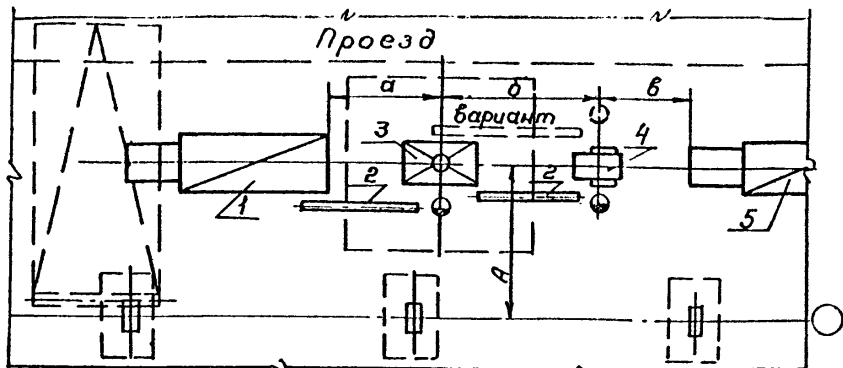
Схема расположения штамповочных линий на базе ПЭМ:
